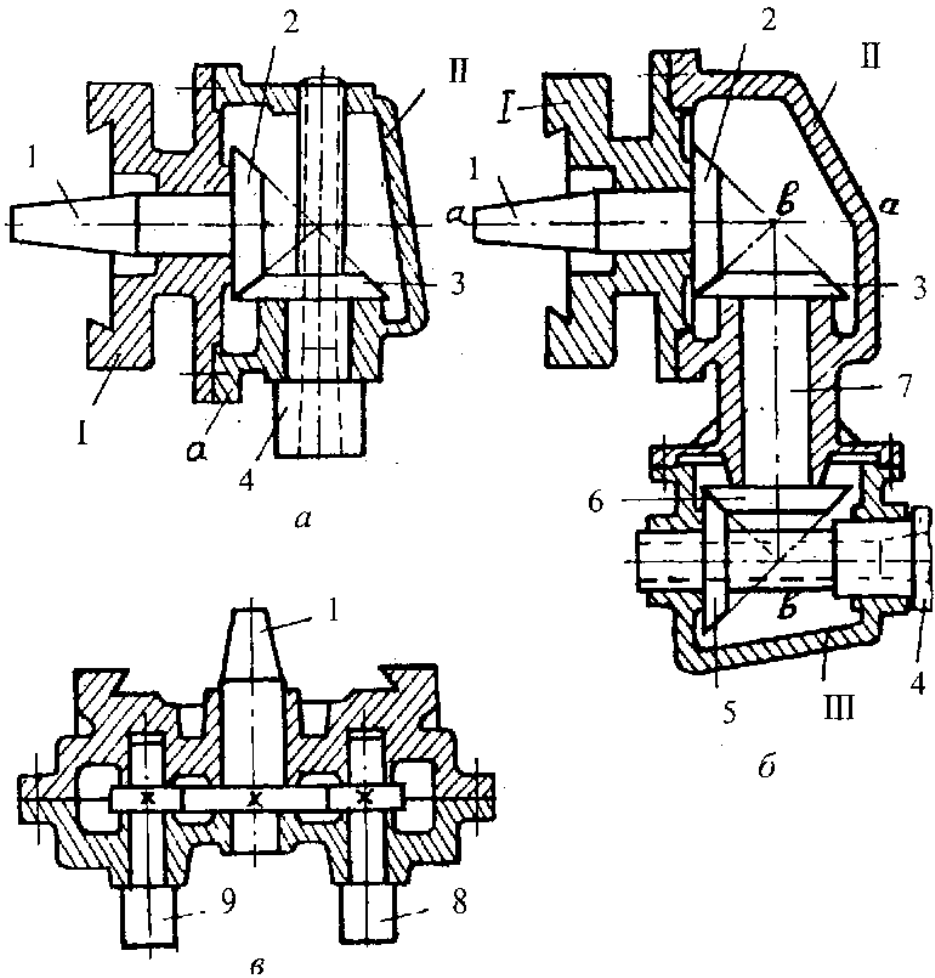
Схеми поворотних і багатшпindelних головок до фрезерних верстатів
